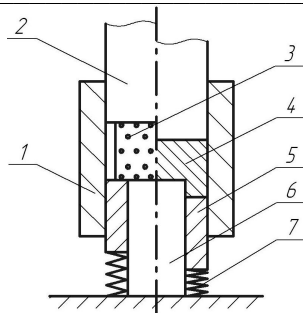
Схема выдавливания: 1 матрица; 2 – верхний пуансон; 3 – прессовка; 4 – деталь; 5 – противодавление; 6 – контрпуансон
